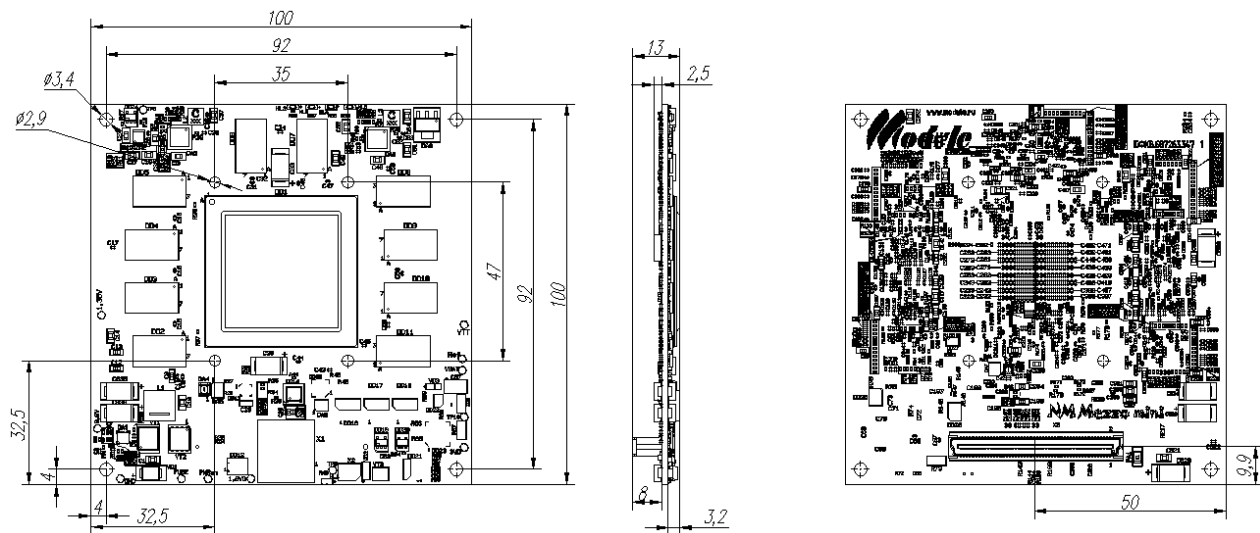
Габаритные и присоединительные размеры Модуля
